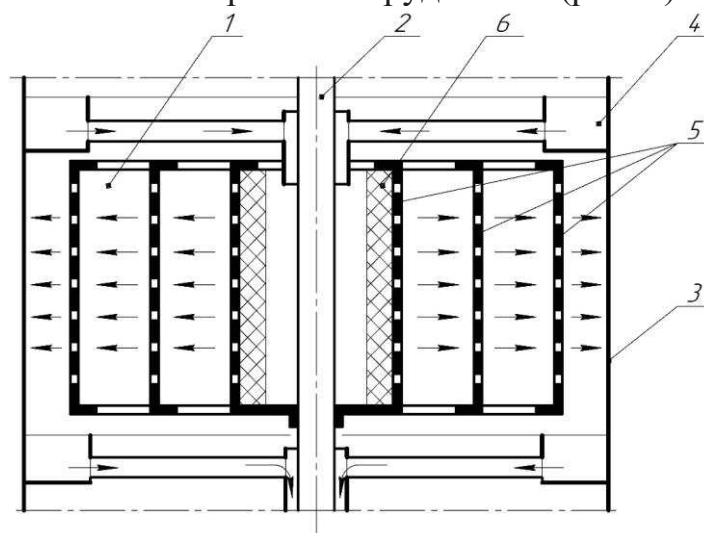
Схема ротормассообменного аппарата: 1 – ротор; 2 – вал; 3 – корпус аппарата; 4 – переливное устройство; 5 – перфорированные цилиндры; 6 – перераспределительный элемент
